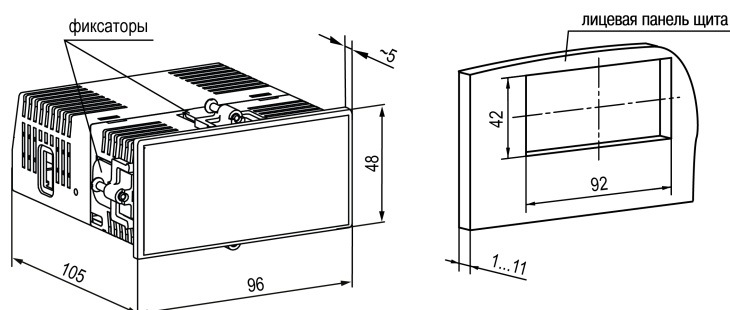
Габаритные размеры корпуса Щ2 и монтажного отверстия в щите
